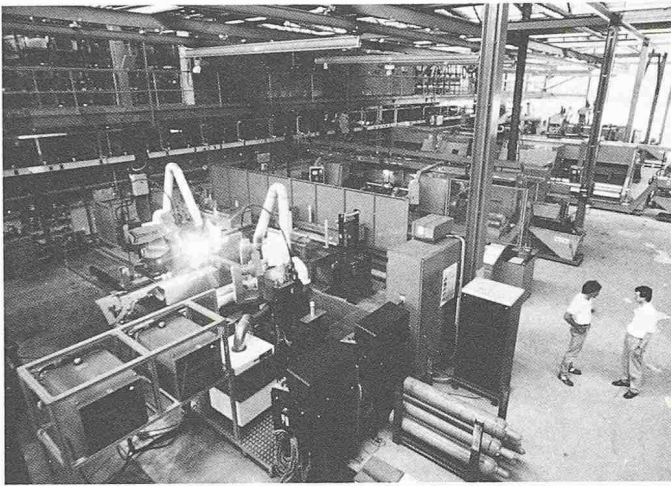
Teilefamilie Walzen: Teilansicht des Lagergestelles und der CNC-gesteuerten Werkzeugmaschine; im Vordergrund eine automatisierte Schweißmaschine mit Roboter
